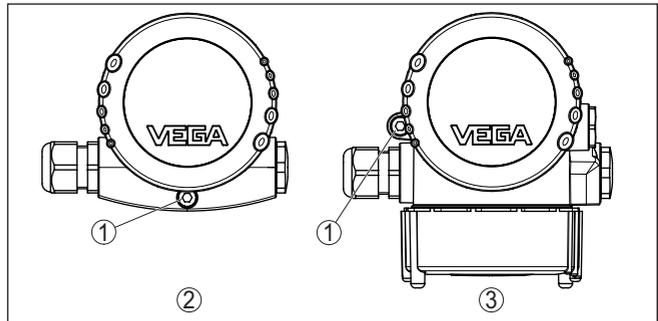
Position der Sicherungsschraube je nach Gehäuse
